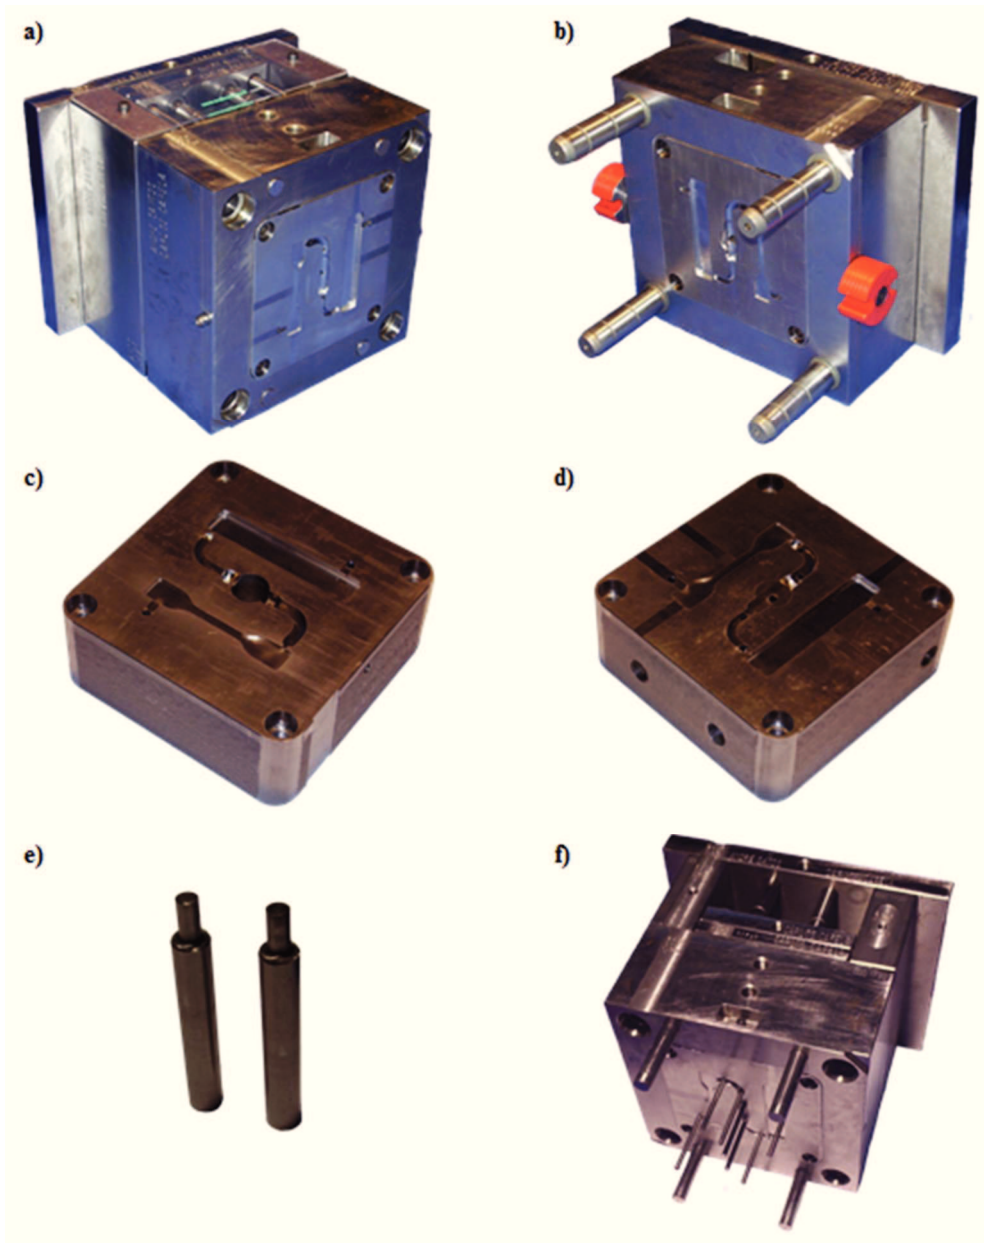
Molde dos provetes; a) lado da extração – lado móvel; b) lado da injeção – lado fixo; c) cavidade; d) bucha; e) postigos moldantes; f) lado móvel com a extração avançada.
